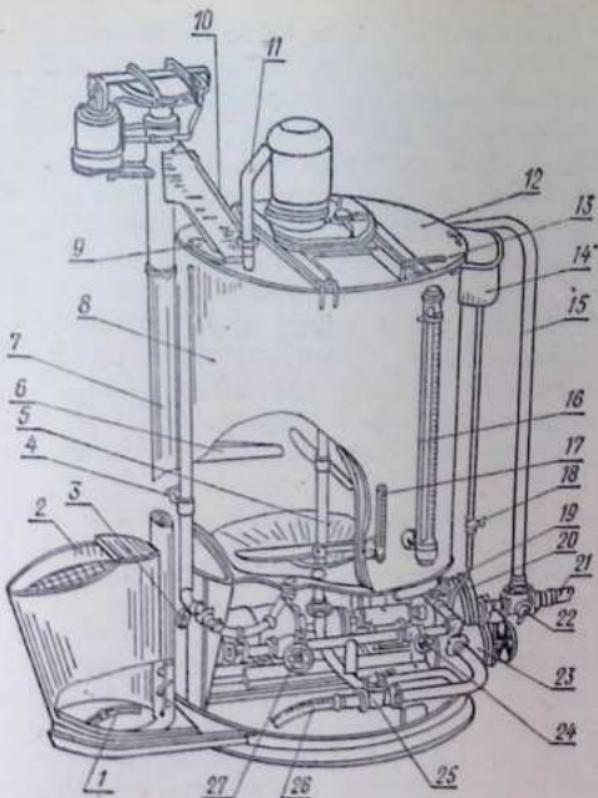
Устройство для приготовления заменителя молока АЗМ-0,8:
